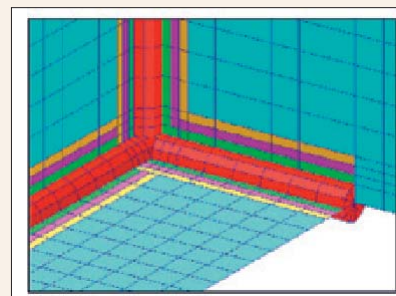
Soldadura en una esquina incluyendo ZBS y ZATs
